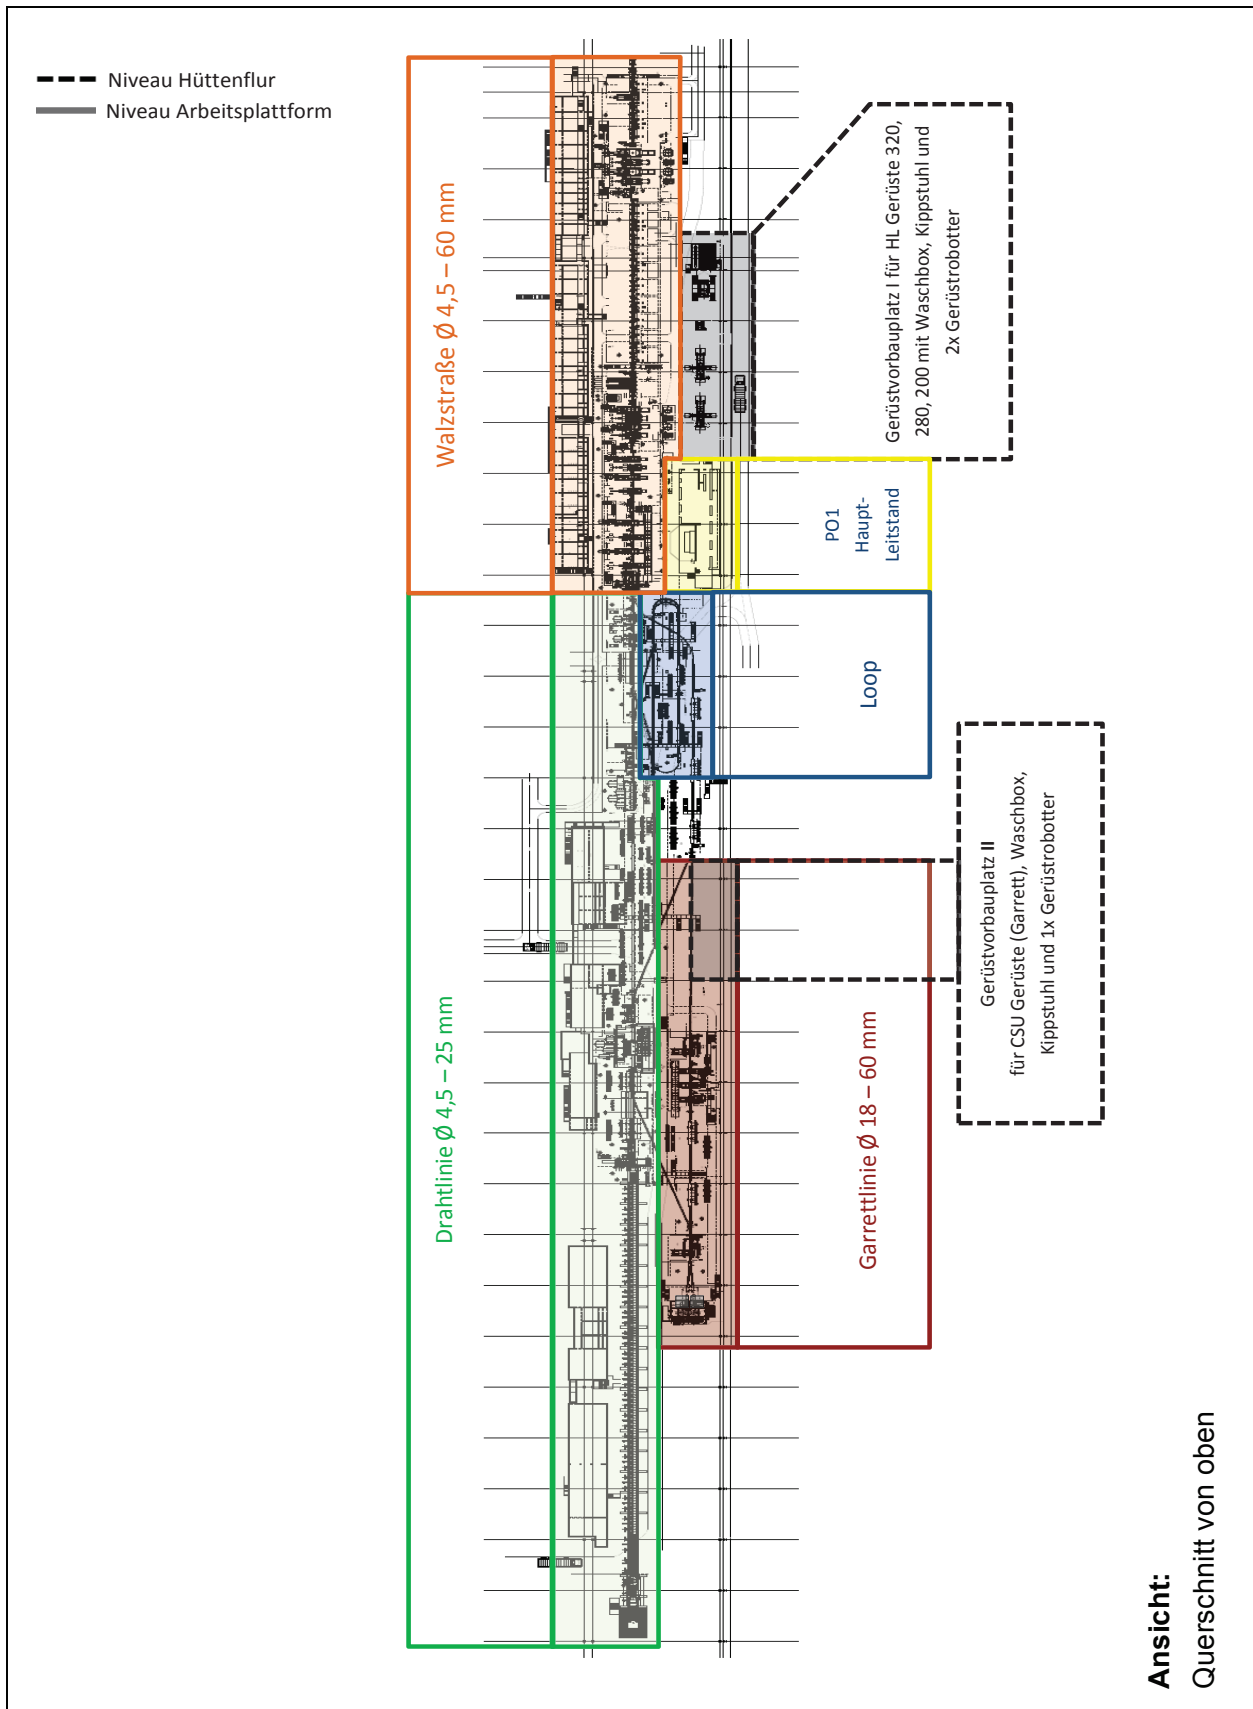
Aufbau Drahtwalzstraße¹⁴⁰
